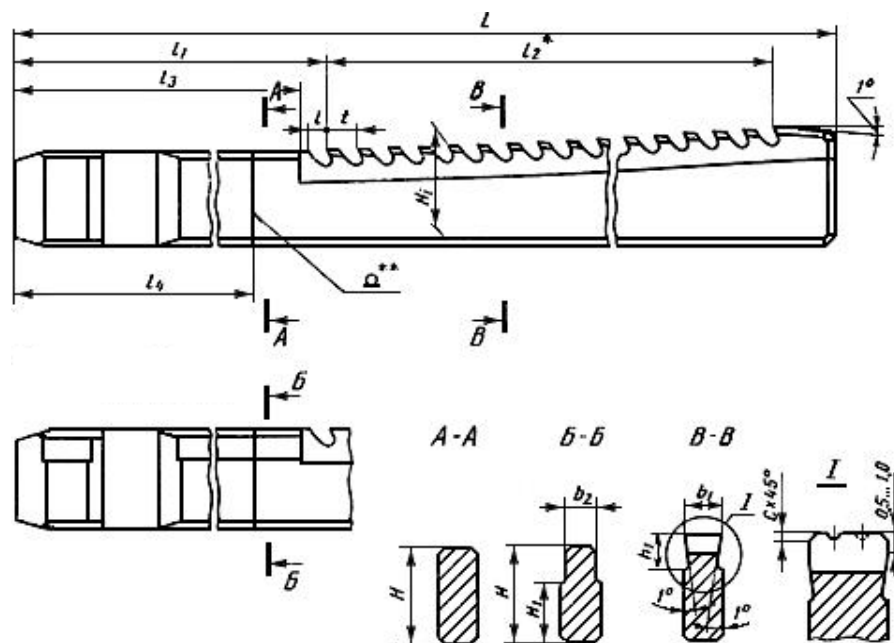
Основні конструктивні розміри шпонкової протяжки
